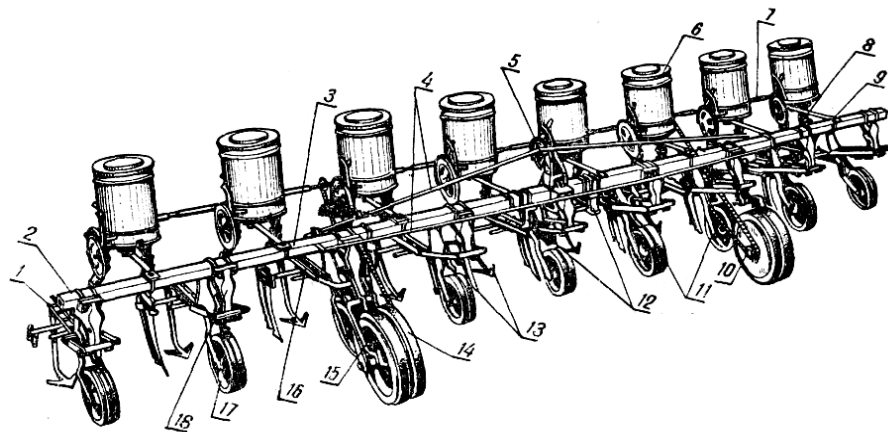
Культиватор-растениепитатель КРН-5,6: 1— секция; 2 — приставка бруса; 3— брус-рама; 4 — шпренгели; 5 — верхний кронштейн навески; 6 — туковысевающий аппарат; 7—соединительная муфта; 8— тукопровод; 9 — кронштейн туковысевающего аппарата; 10 — ведущая звездочка (2=7 или 2 = 14); 11— приводная цепь; 12 — нижний кронштейн навески; 13 — рабочие органы; 14 — опорное колесо; 15 — стойка опорного колеса; 16 — грядиль; 17 — опорное колесо секции; 18 — кронштейн крепления секции; 19 — планка звена; 20 — нижнее звено четырехзвенника; 21 — скоба; 22 — регулируемое звено четырехзвенника; 23 — ограничитель опускания; 24 — задний кронштейн; 25—накладка с держателем; 26 — накладка с призмой; 27 — брус с боковым держателем; 28 — задний держатель; 29 — срезной
